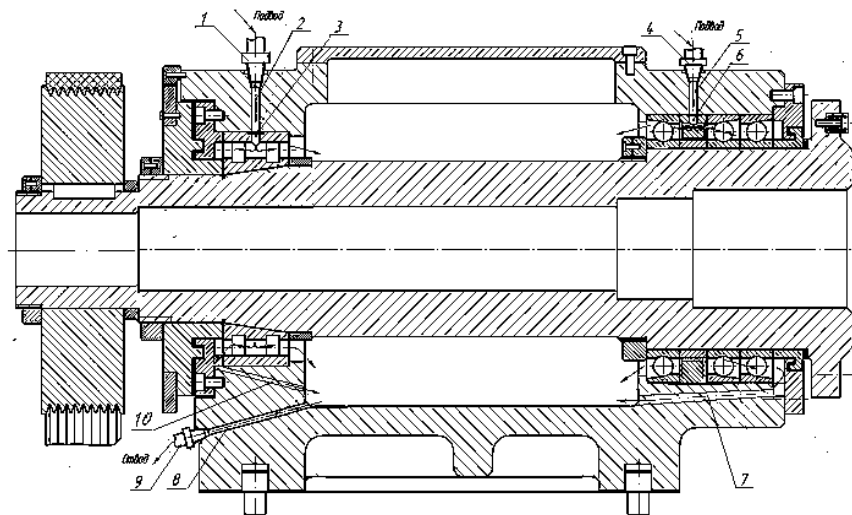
Автономная шпиндельная бабка токарного станка с каналами для циркуляционного смазывания подшипников шпиндельных опор
